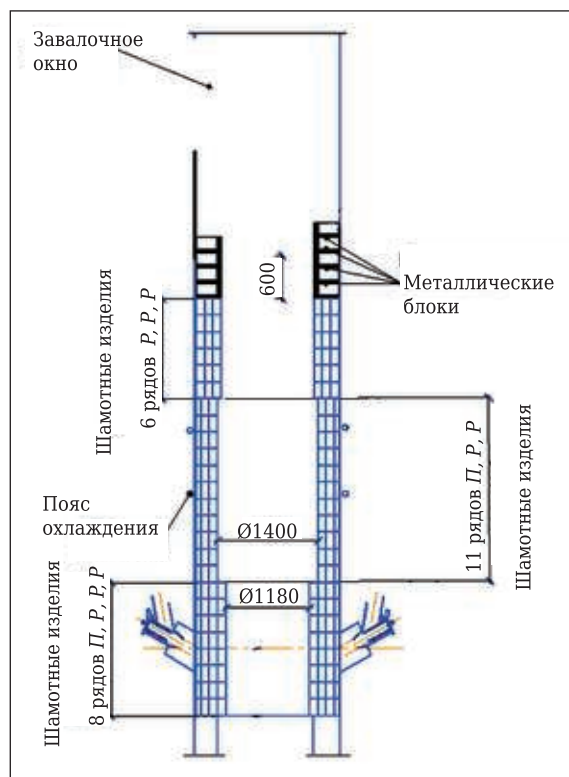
Схема футеровки коксогововой вагранки: П — изделия прямые шамотные ваграночные № 3 марки ШБ; Р — клин ребровой ваграночный шамотный № 2 марки ШБ
